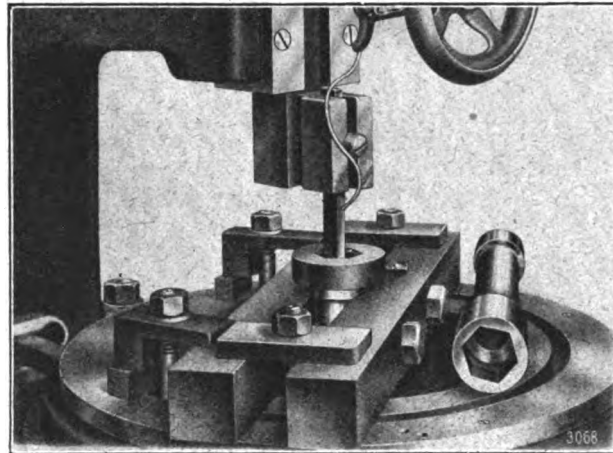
Innenbearbeitung eines Sechskantschlüssels.
